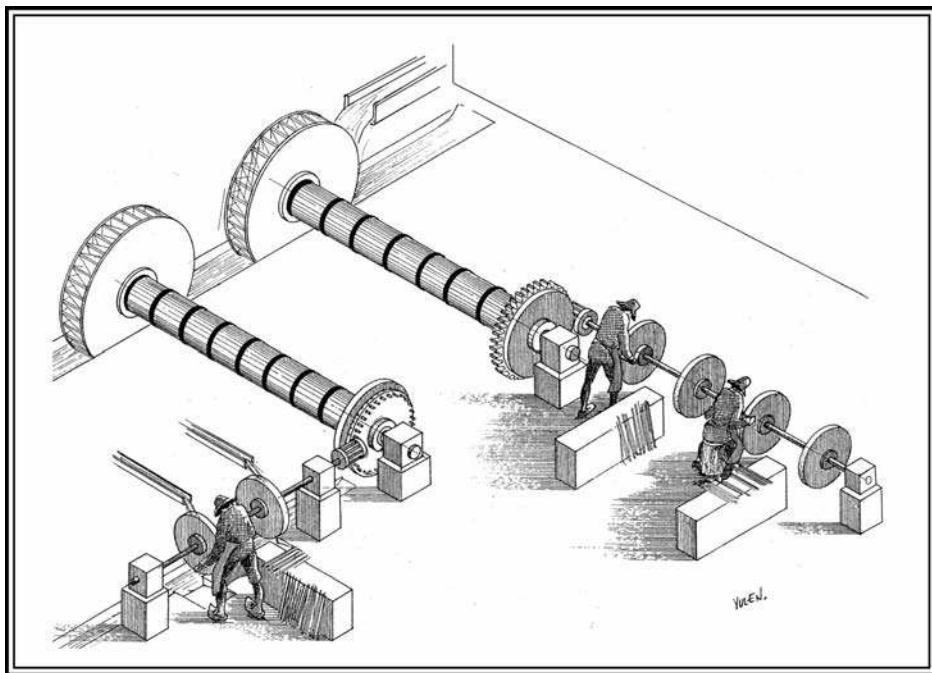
Conjunto industrial. (Dibujo Julen Zabaleta).
